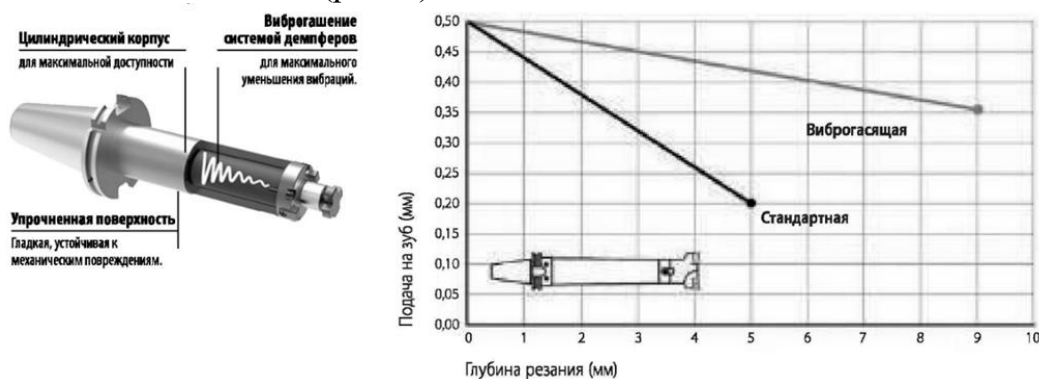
Виброгасящая оправка для насадных фрез с торцовыми шпонками
